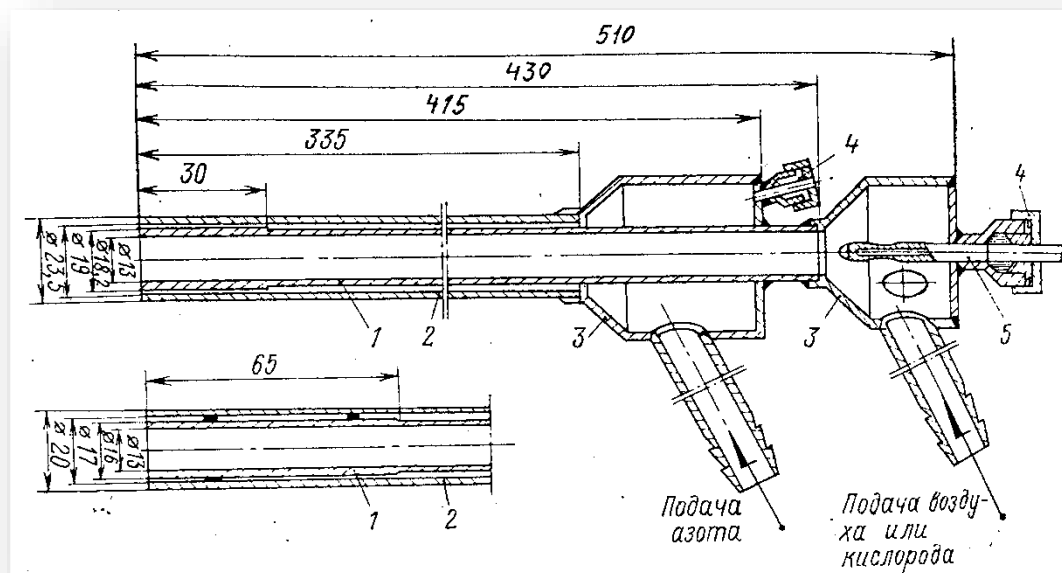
Конструкция ФЗО для плавки медно-никелевых руд [85]
